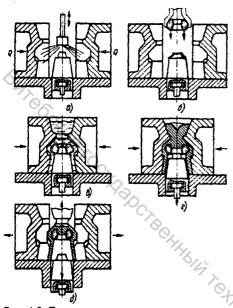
Последовательность изготовления отливки в кокиле:
